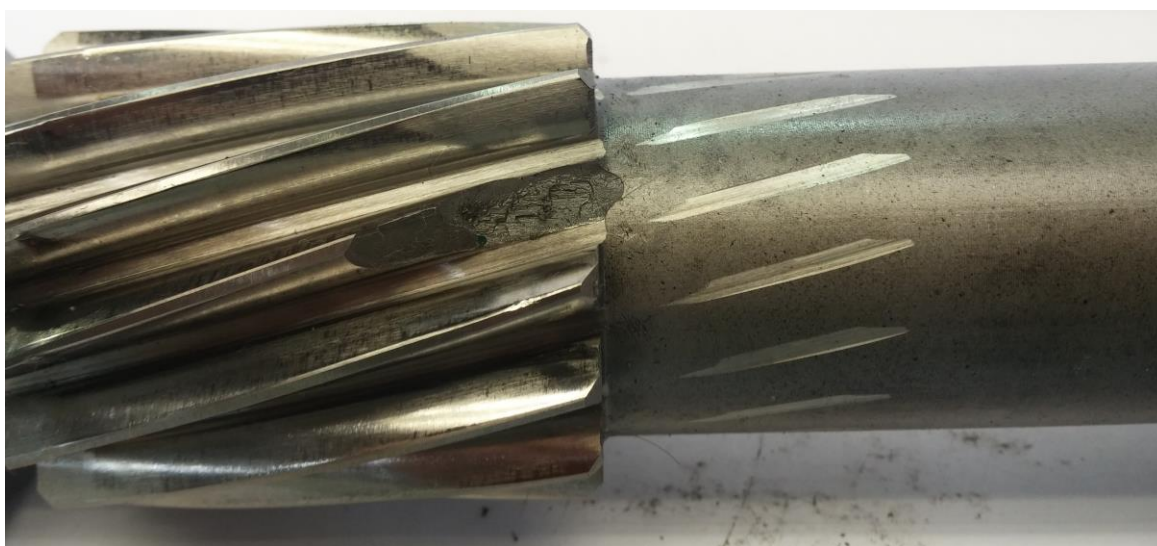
Внешний вид входного вала-шестерни редуктора с эвольвентным зубчатый зацеплением после испытаний
